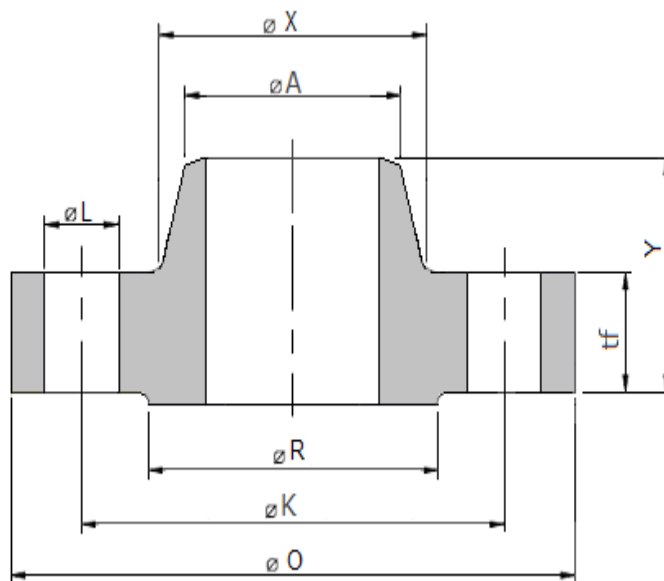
Croquis brida empernada. Fuente: DN Brida, "Brida Welding Neck ANSI/ASME B16.5 Class 600 lbs"
